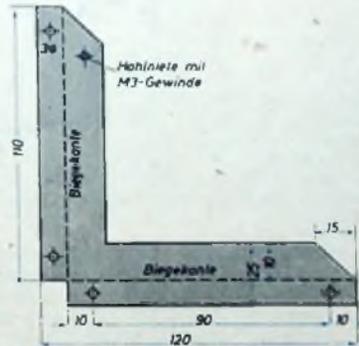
Haltewinkel für die Frontplatte. Material: 1 mm verzinktes Eisenblech
